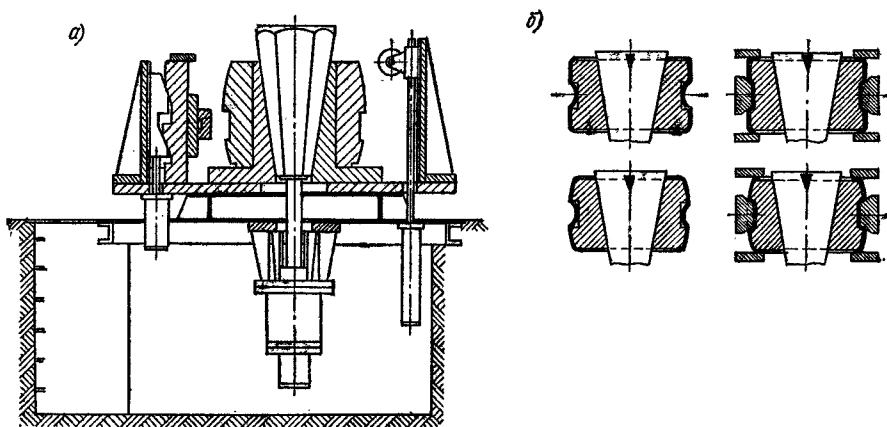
Гидравлическая установка для растяжки крупных деталей: а — схема установки; б — схемы рабочих инструментов
